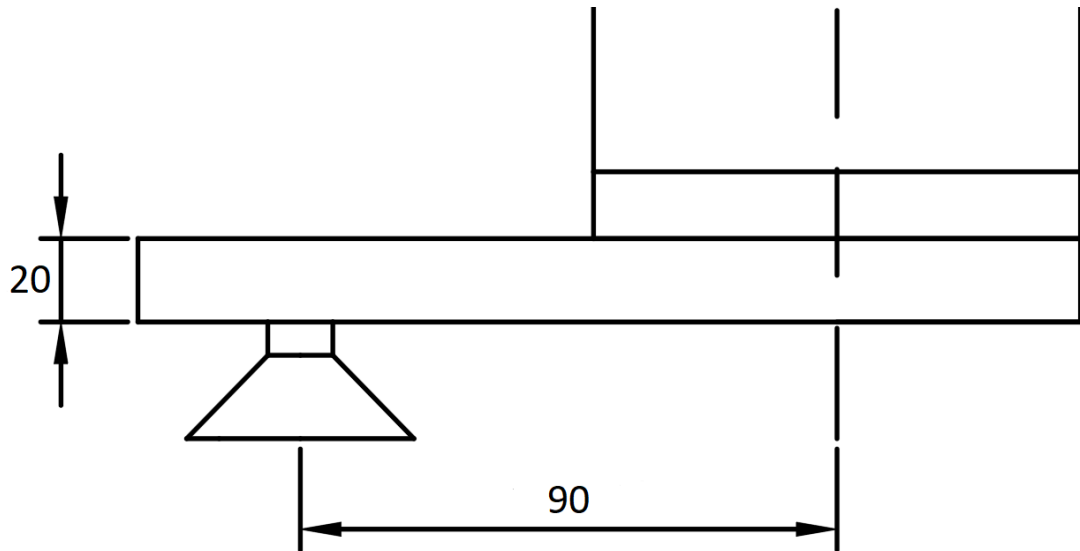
Розміри для налаштування точки центра інструменту
